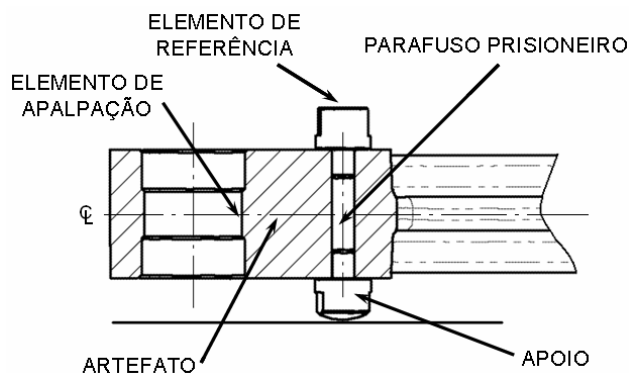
Detalhe da montagem do sistema de apoio para posição horizontal.
